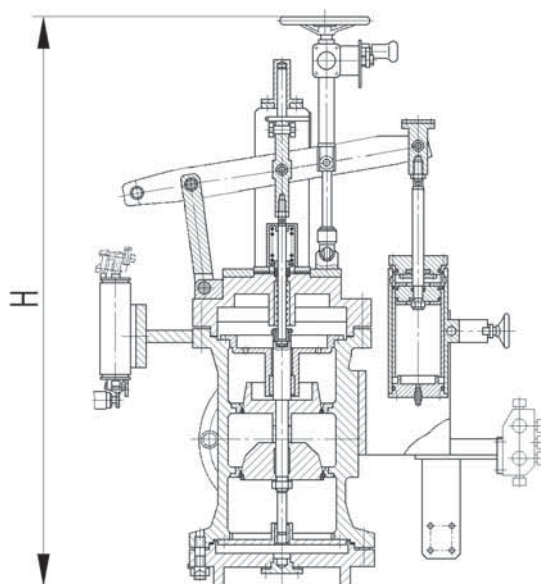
Клапан регулирующий проходной фланцевый с гидроприводом
